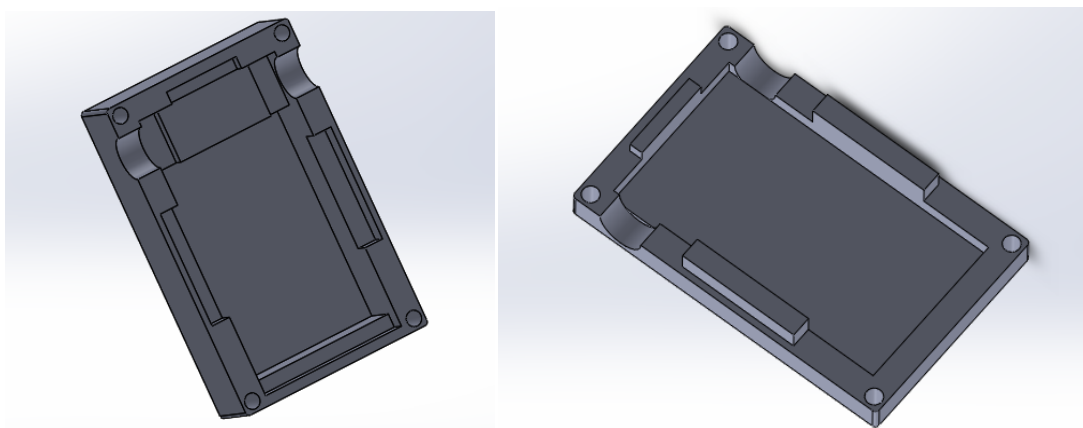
Desenho da parte inferior do invólucro em 3D com correções
